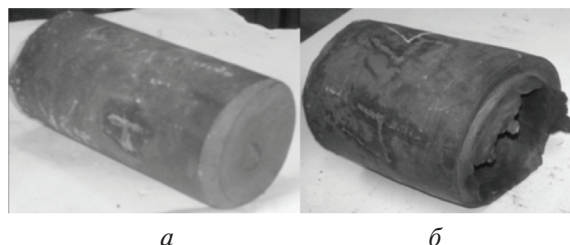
Фото задних концов обжатой заготовки и гильзы
